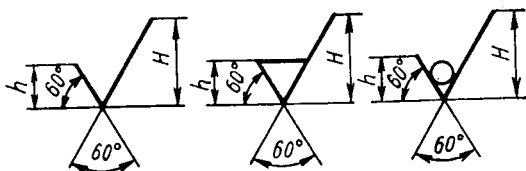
Условные знаки для изображения шероховатости поверхностей
